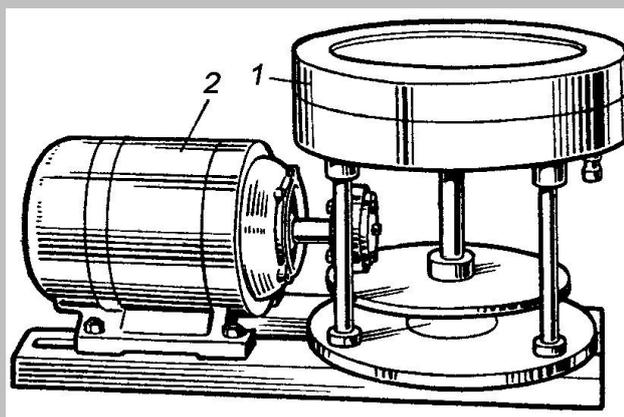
Шлифовальный станок: 1 – металлический круг; 2 – электродвигатель.
